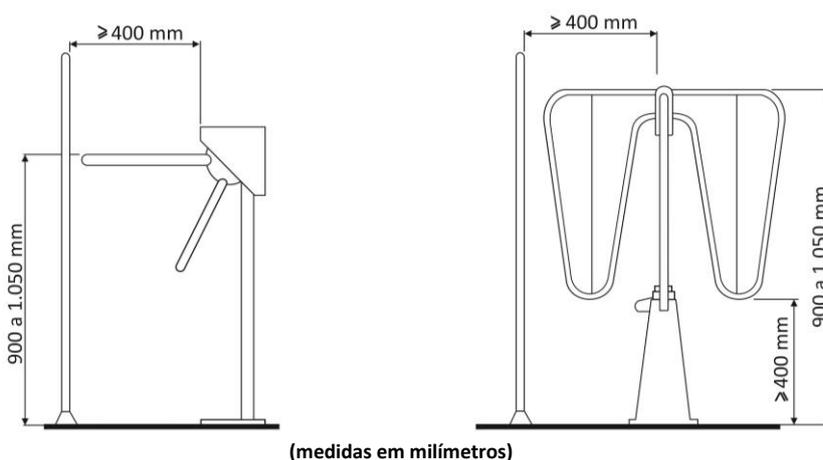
Dimensões do dispositivo de contagem de passageiros
